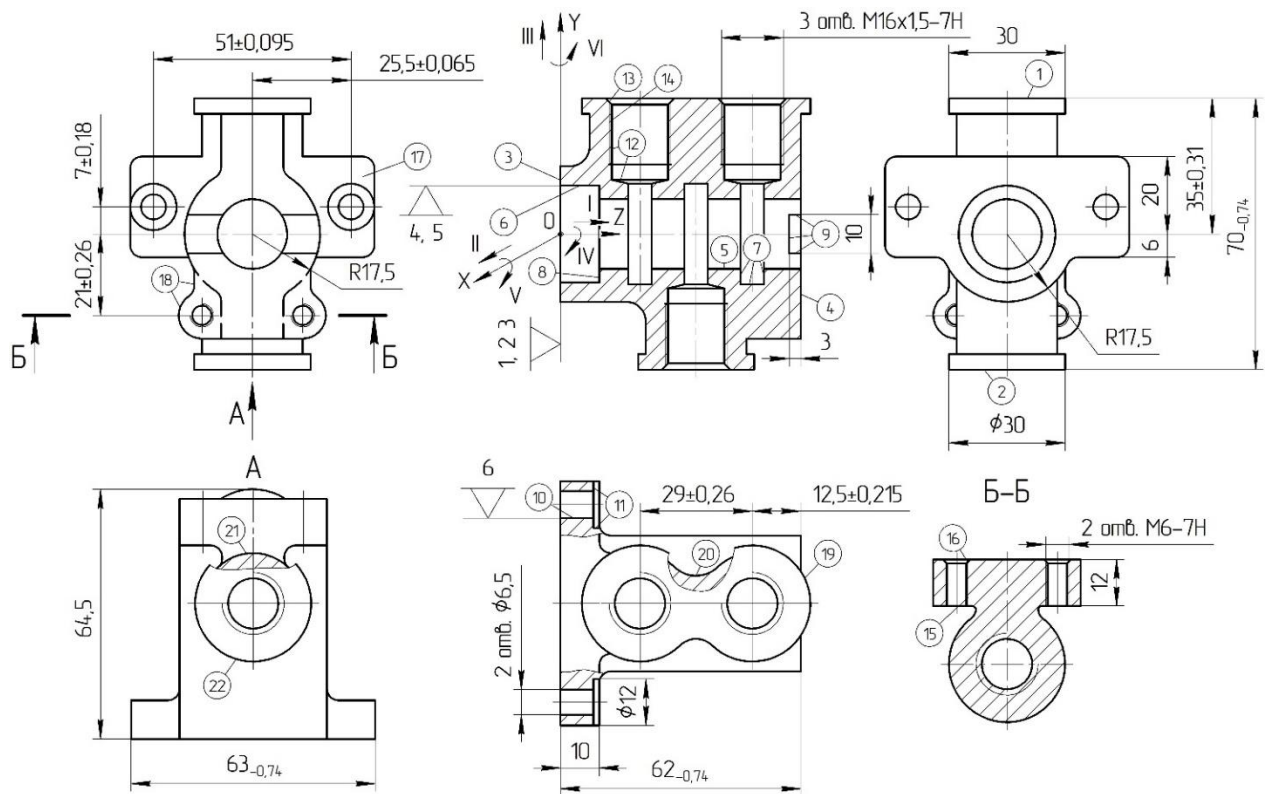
Ескіз корпусу золотника із нумерацією поверхонь
